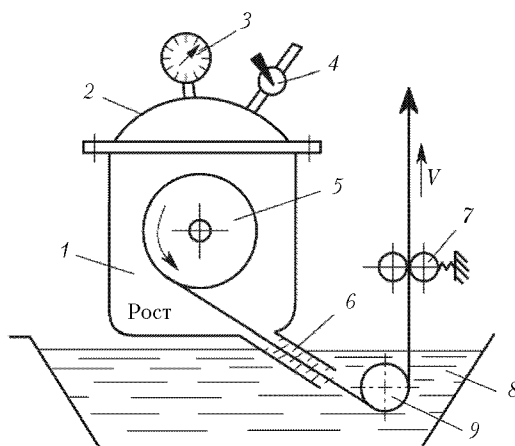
Схема установки для вакуумной пропитки волокнистого наполнителя
